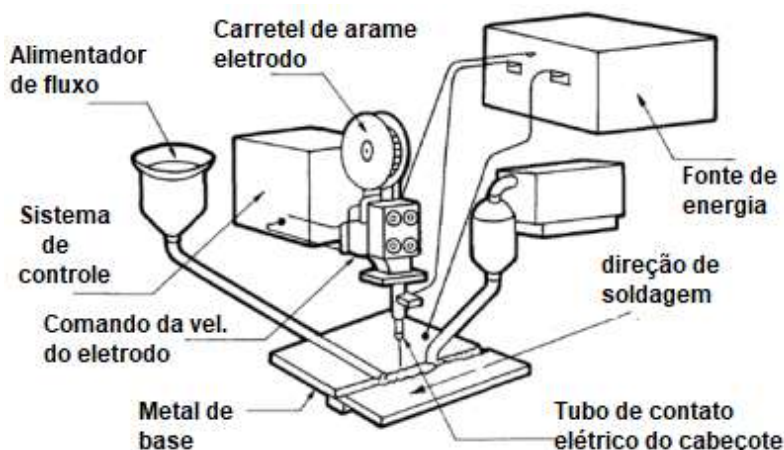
Equipamentos de Soldagem a Arco Submerso. Fonte: Adaptado de [Wainer et al. 1992]
